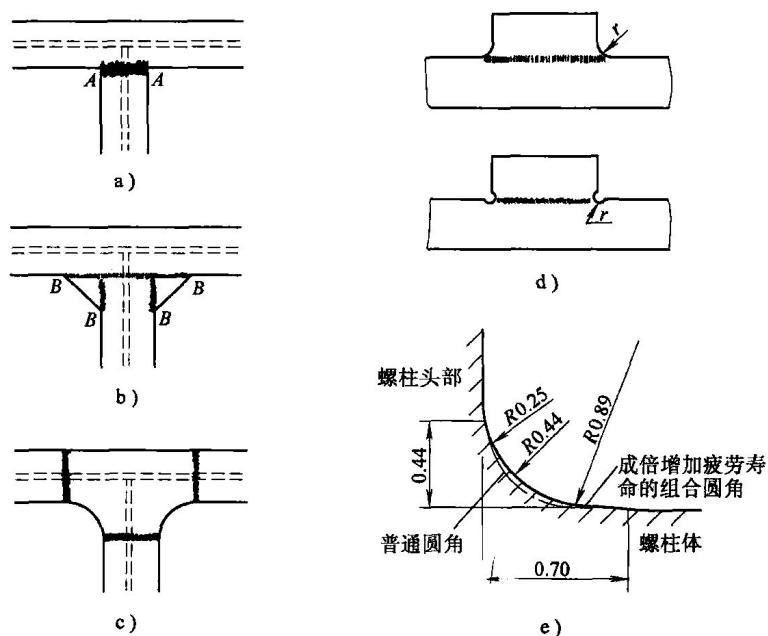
焊接结构及零件截面几何形状的改变
